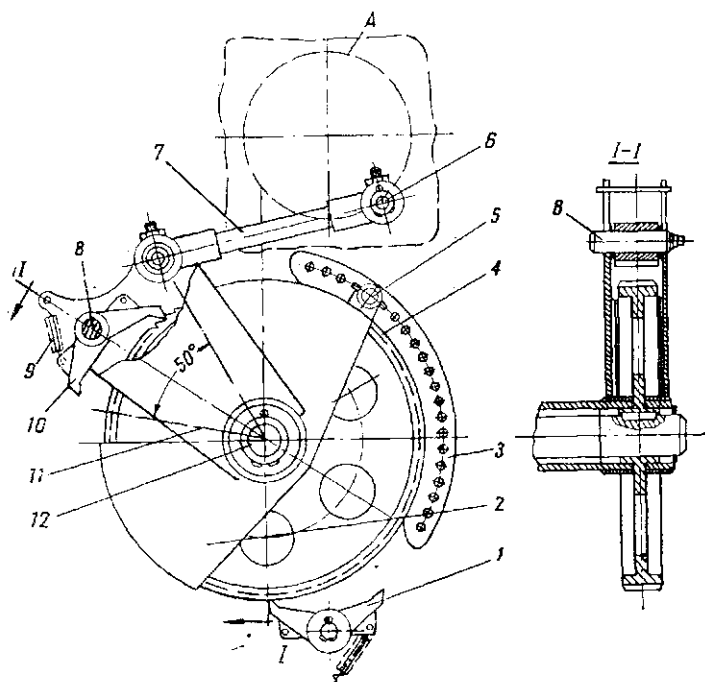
Схема кривошипно-шатунного и храпового механизмов приводного устройства продольного транспортера кормораздатчика ПТУ-10К:
